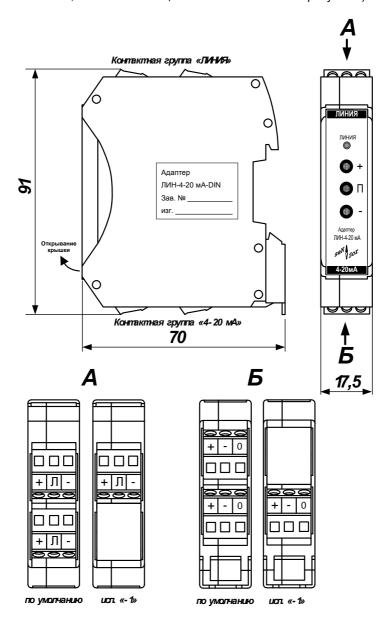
Адаптер. Внешний вид, габаритные размеры.
